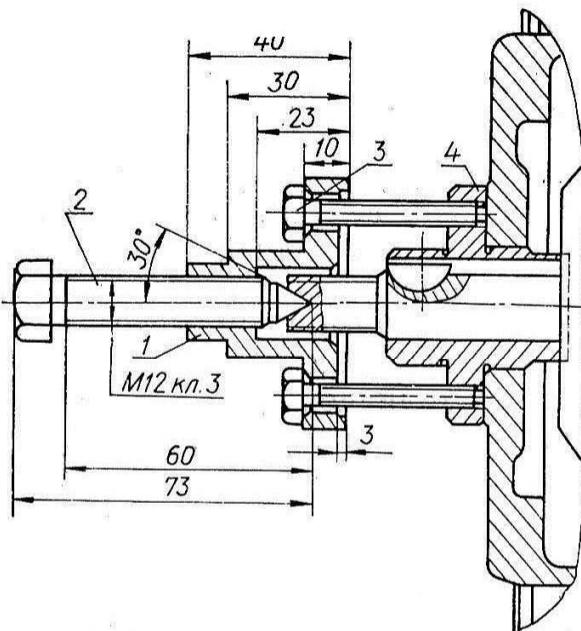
Съемник для снятия рабочего колеса вентилятора с вала генератора:
